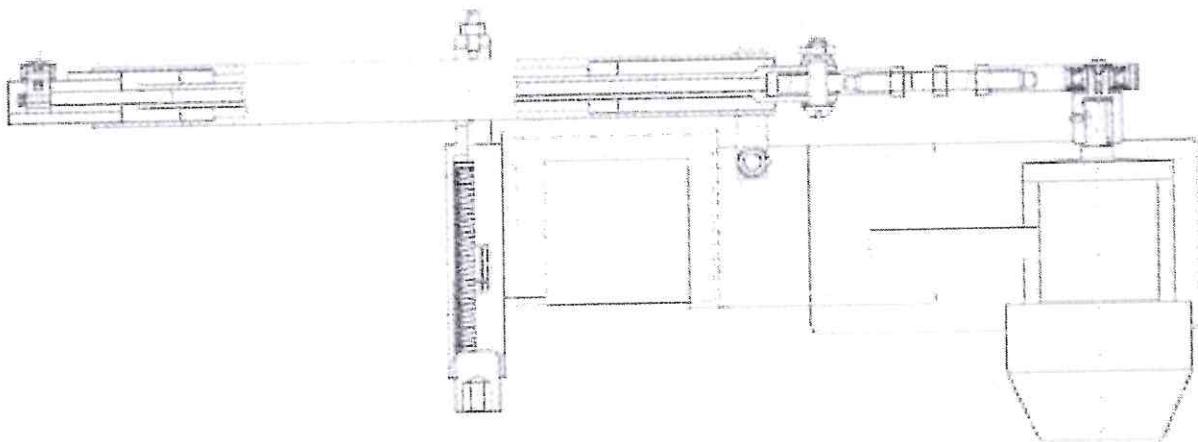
Предлагаемая головка для виброобкатывания .
